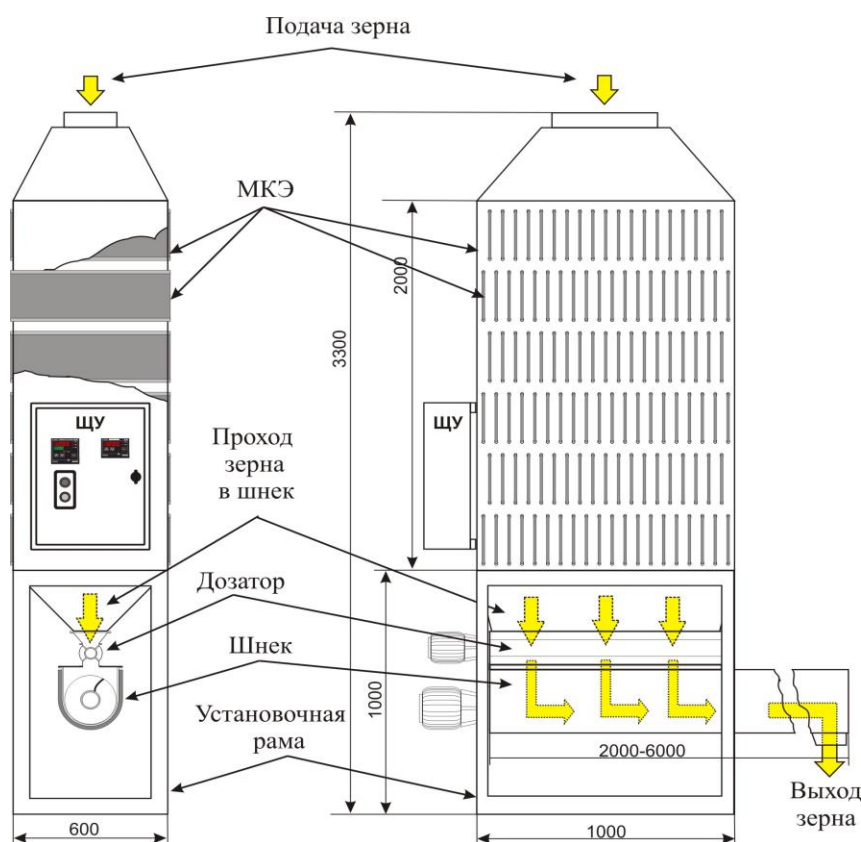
Основные блоки и габаритные размеры ЭАПЗ
